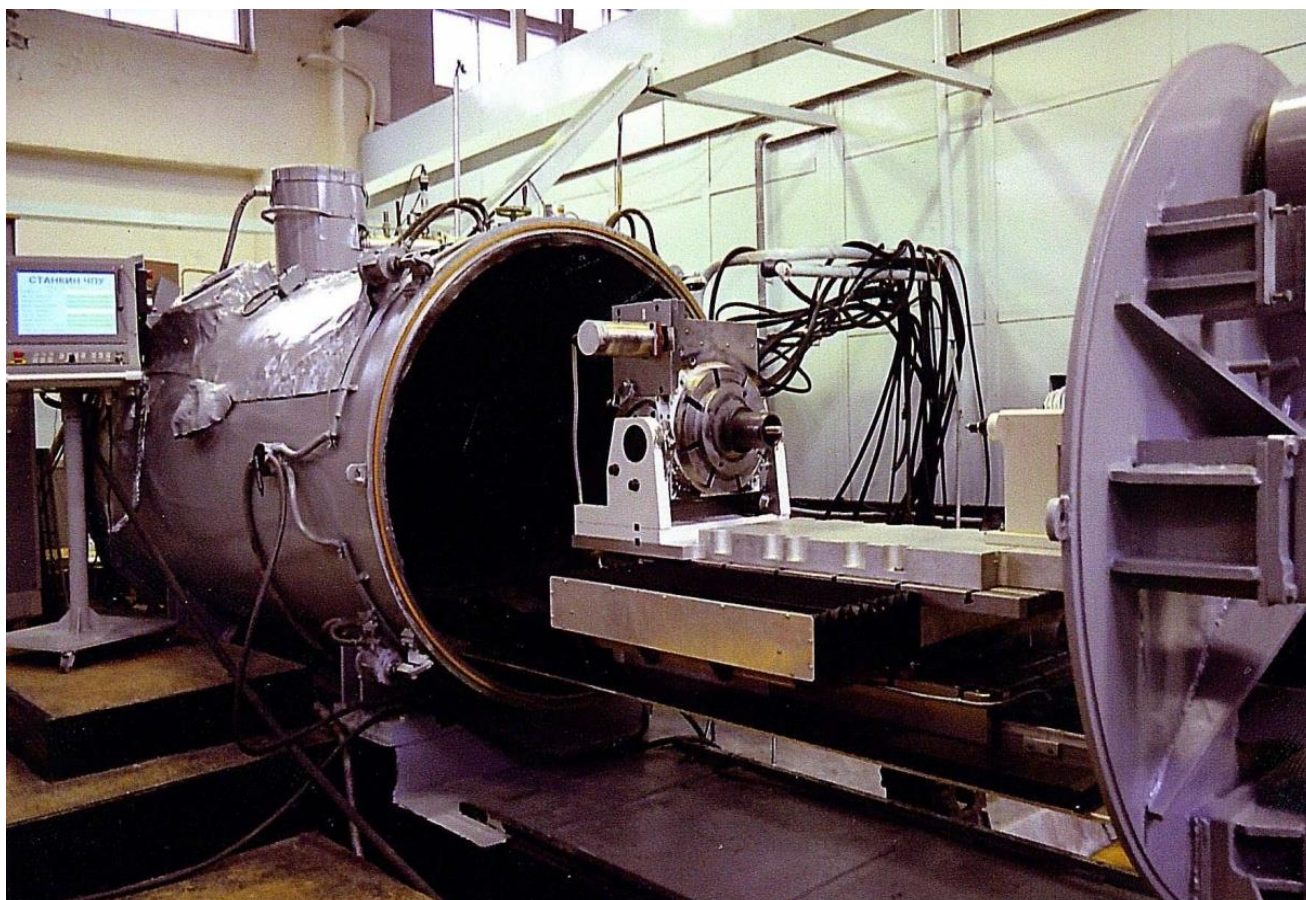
Установка для ЭЛС на базе камеры ЭЛУ-9А
